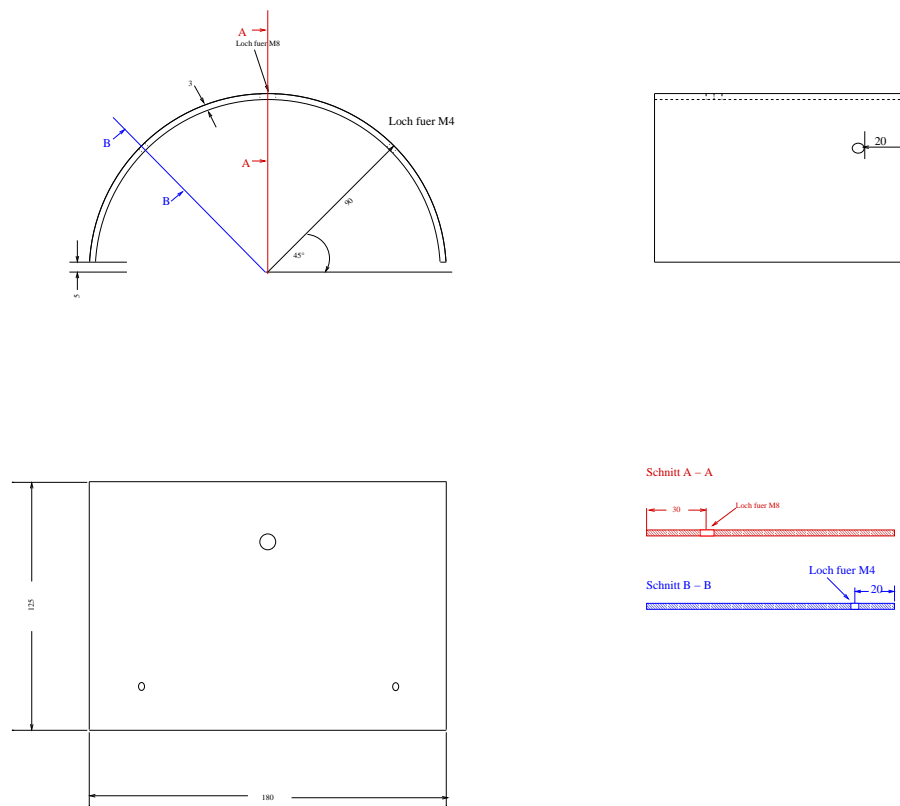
Erdtrichter G2. Dargestellt ist einer der Erdtrichter G2. Die beiden Hälften werden von je zwei Edelstahlwinkeln gehalten, die an die Tankwand geschweißt wurden. Die Spannungszuführung besteht aus Stahldrähten die mit einem Glasrohr ummantelt sind. Der Schlitz zwischen beiden Hälften verläuft vertikal.
